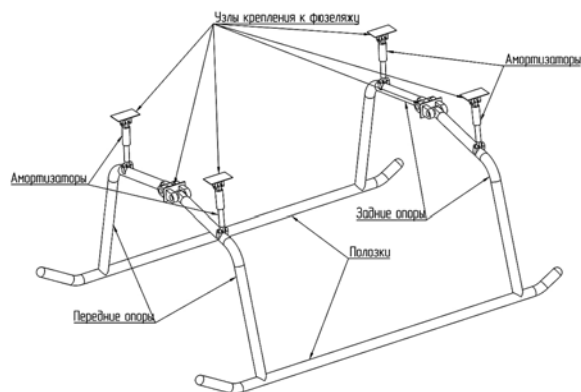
Полосковое шасси рычажного типа с выносным амортизатором
